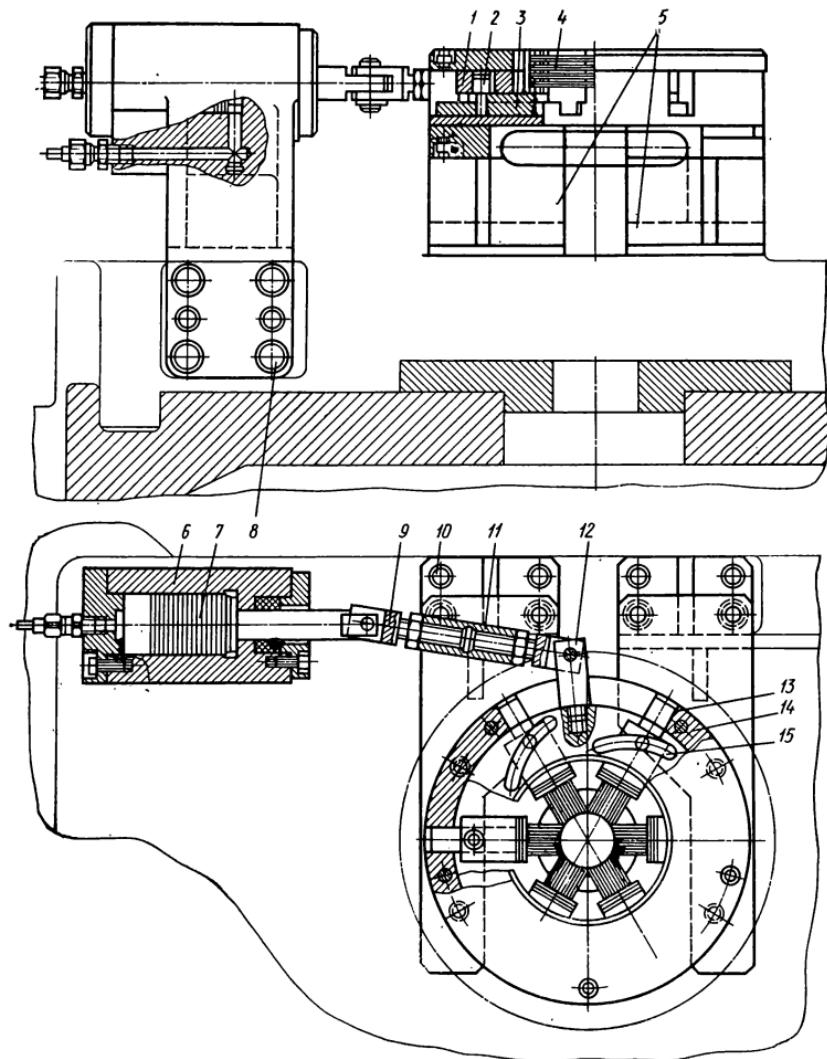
Автоматическое приспособление для очистки протяжек от стружки:
